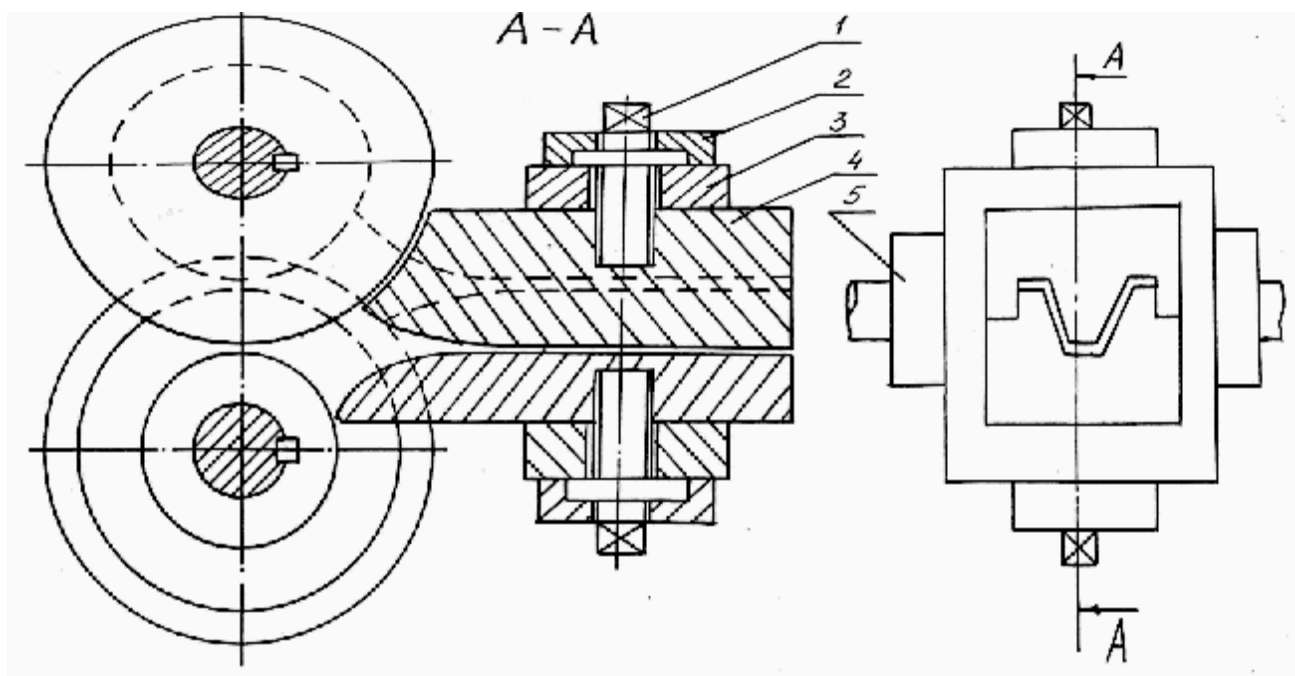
Фильера правильная: 1 – винт; 2 – крышка; 3 – корпус; 4 – фильера; 5 – коромысло
